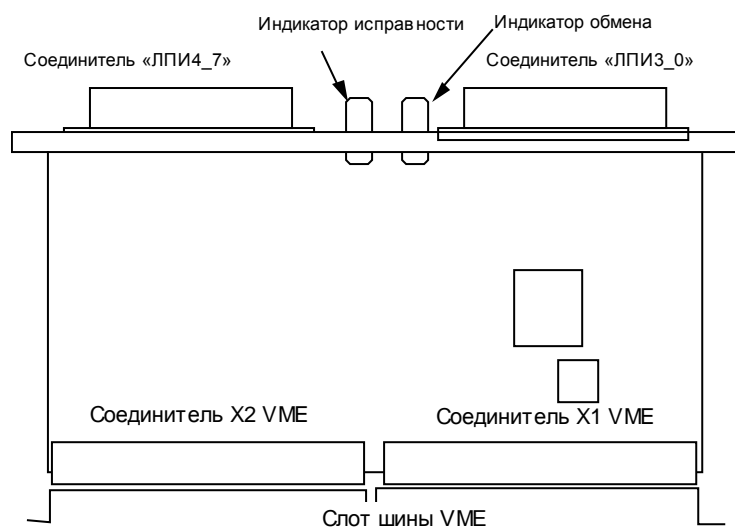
Внешний вид и способ установки УСМК 9V-8
